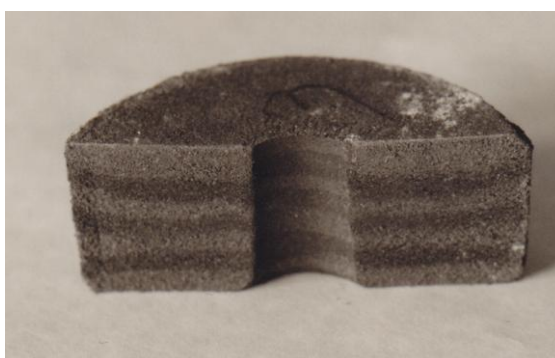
Образец, полученный прессованием из одинарной пакетной заготовки по схеме: предварительное прессование – переворот на 180° – окончательное прессование
